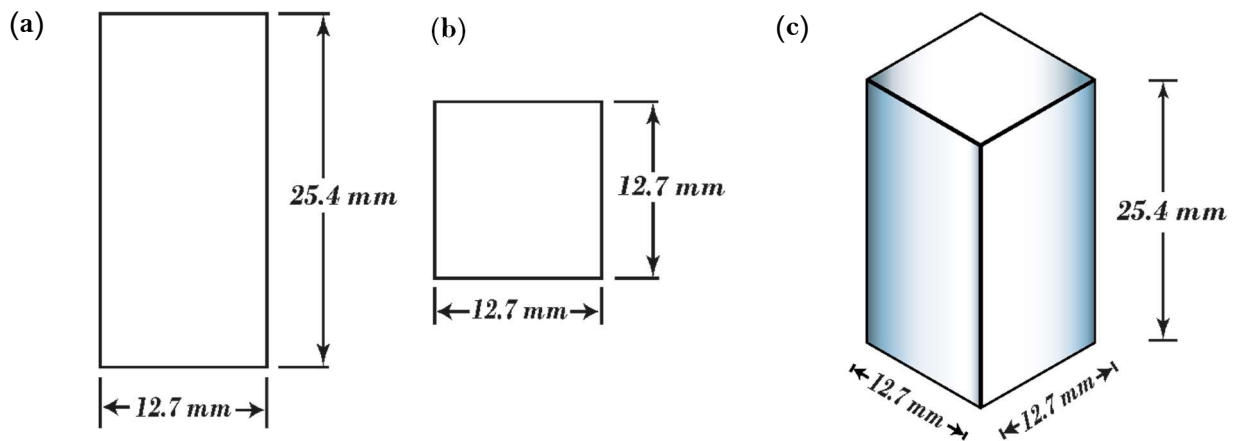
Dimensiones del espécimen estándar para ensayo de compresión: (a) Vista frontal; (b) Sección transversal del espécimen; (c) Vista isométrica.
